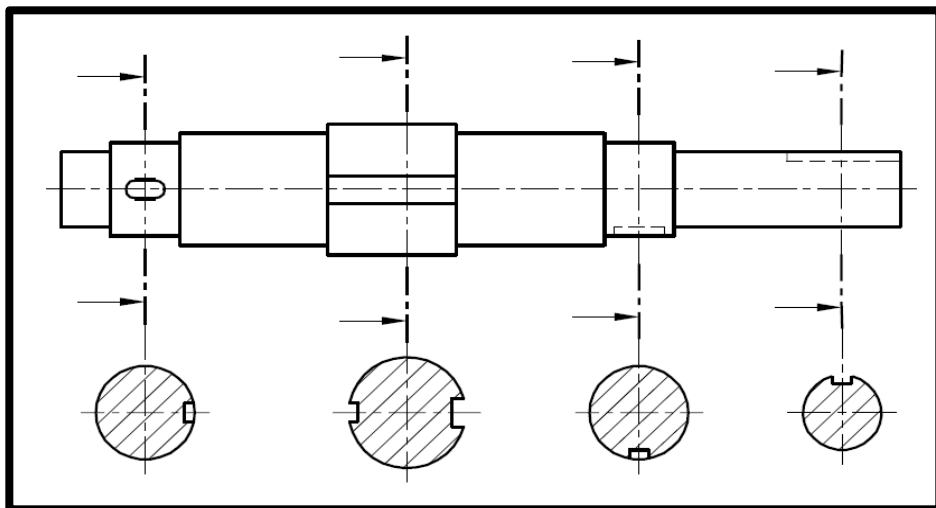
Sezioni successive su un albero poste sul prolungamento delle tracce dei piani di sezione; non occorre l'indicazione dei piani di sezione
